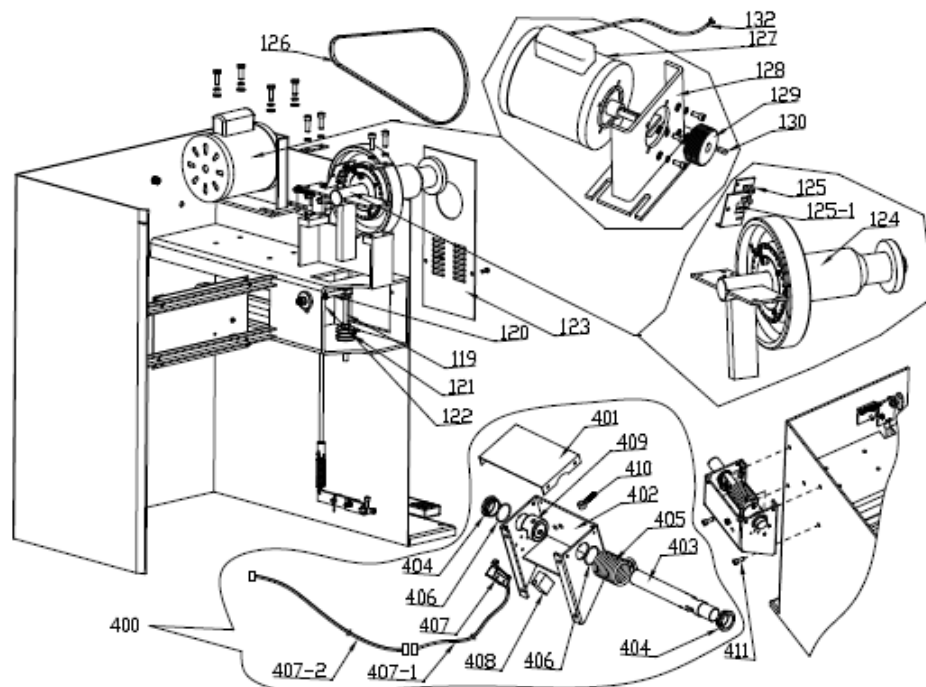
Subsistema 2, despiece COMPUTER BOARD ASSY
